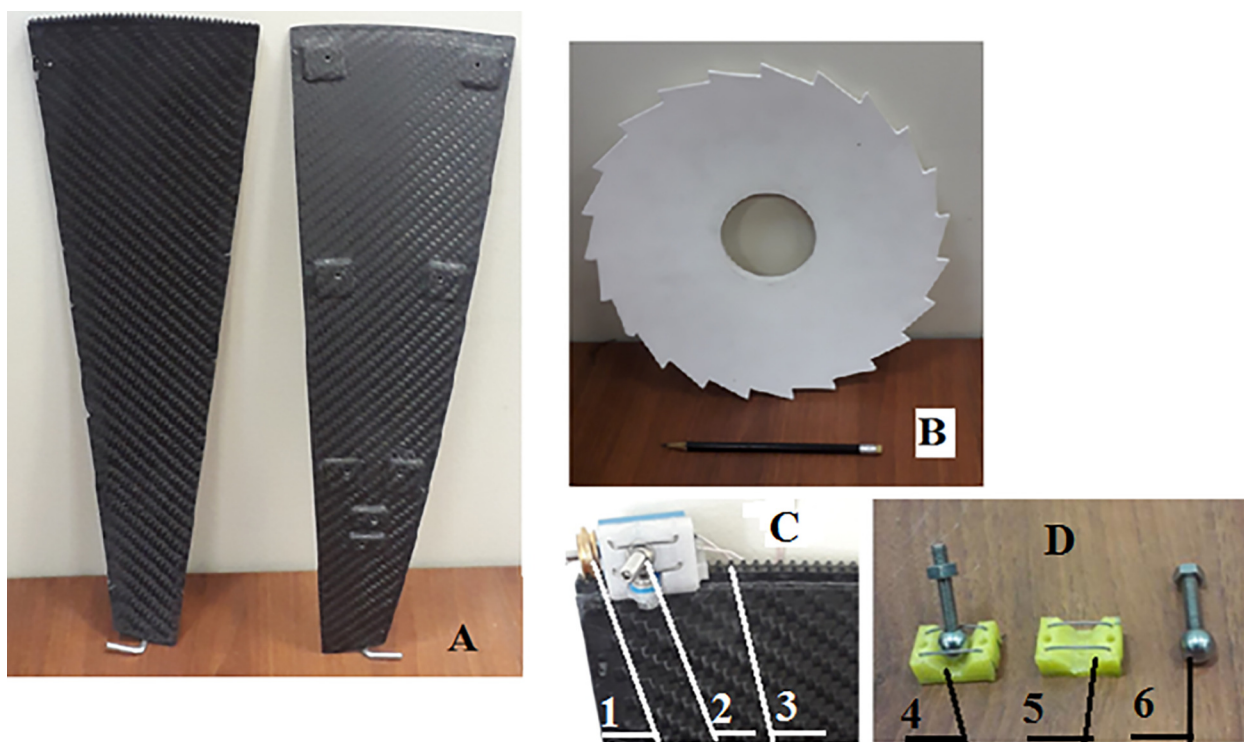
Элементы макета: А – углепластиковые лепестки, В – центральное зеркало, С – линейный исполнительный механизм на кромке лепестка, 1 – линейный исполнительный механизм, 2 – сферический шарнир, 3 – зубчатая рейка червячной пары, D – самоустанавливающийся сферический шарнир; 4 – шарнир в сборе, 5 – V-образный паз, снабженный пружинным захватом, 6 – сферическая опора.
